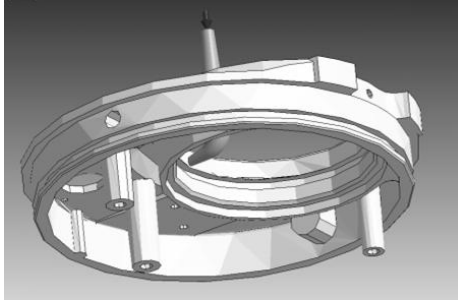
3D-модель анализируемой детали «Корпус»
